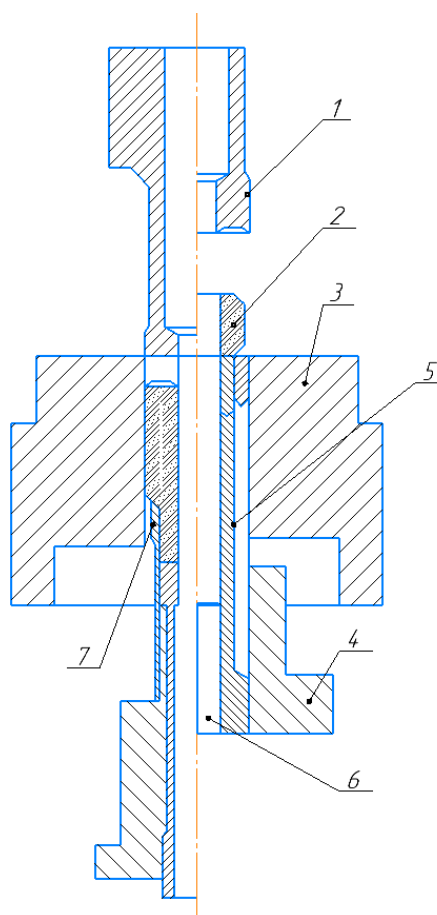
Пресс-форма с дополнительным дренающим зазором: 1 — верхний пуансон; 2 — пористый подшипник; 3 — матрица; 4 — наружный нижний пуансон; 5 — внутренний нижний пуансон; 6 — стержень; 7 — дополнительный дренающий зазор
